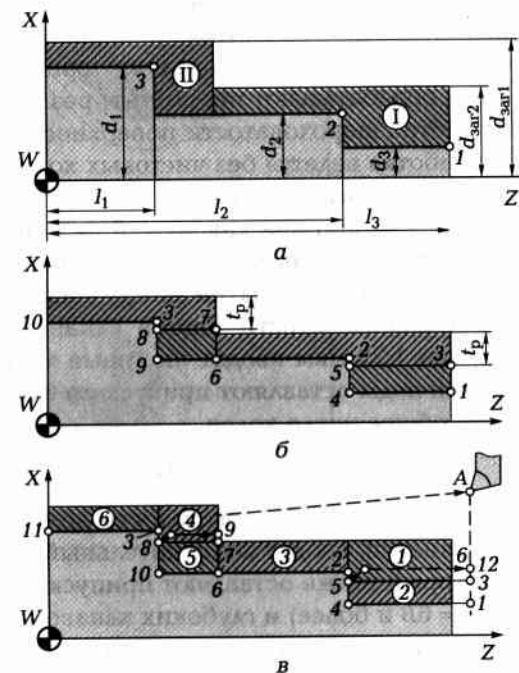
Зона черновой обработки ступенчатой заготовки (а—в)
